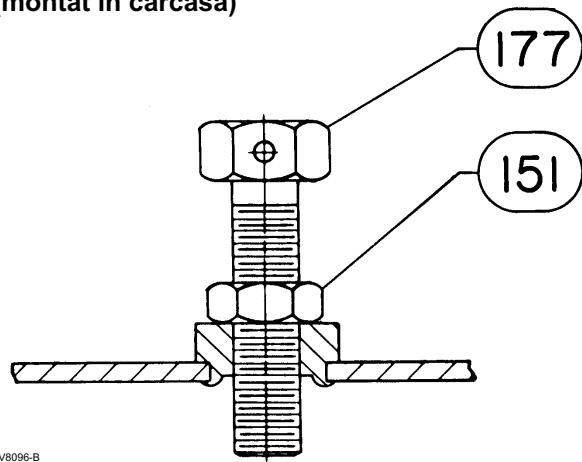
Opritorul cursei de urcare, tip 13 - Pentru dimensiuni cuprinse între 30/30i - 60/60i și pt. dimensiuni de 76/76i, prezentat cel cu dimensiunea de 30/30i (montat în carcasă)
